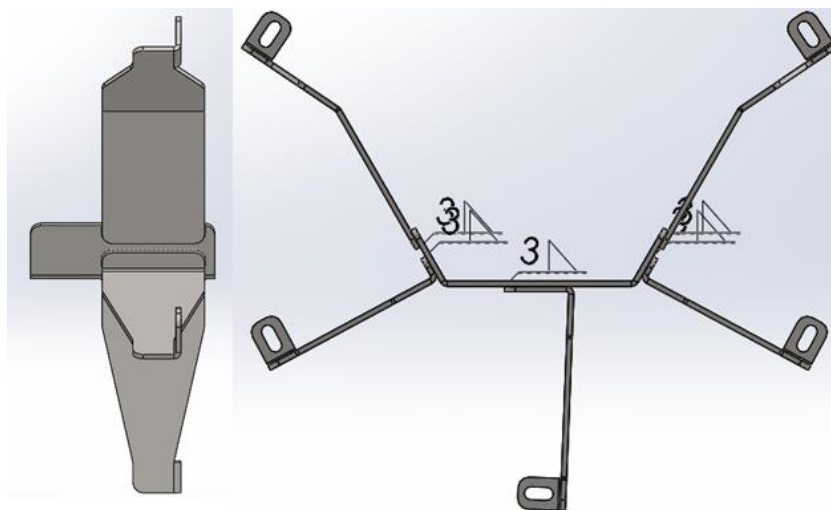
Kit de Ventilação Forçada - "Estrutura aranha" W50 400
